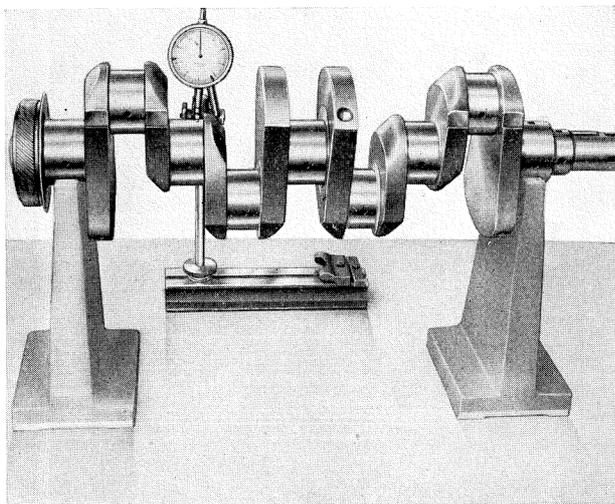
Contrôle de l'alignement des portées du vilebrequin.
